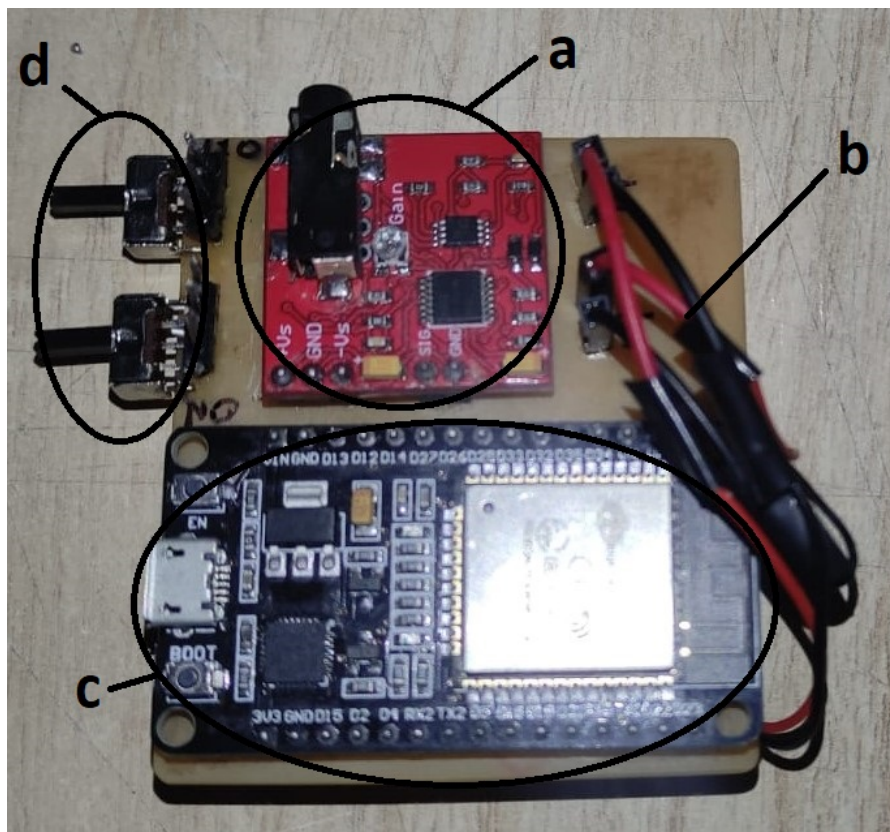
Montaje de los componentes electrónicos en la placa PCB.
